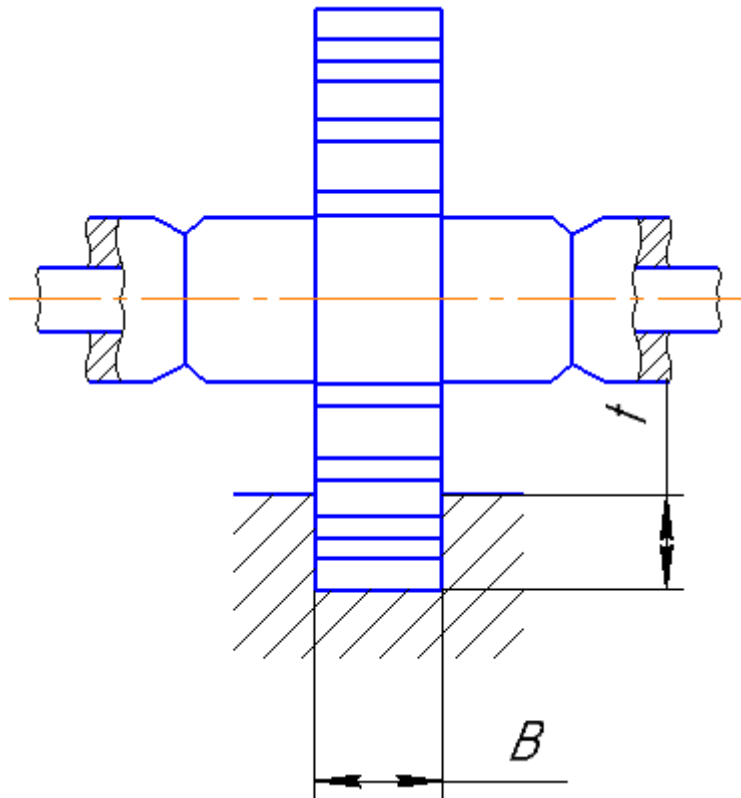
Схема фрезерування пазу дисковими фрезами
